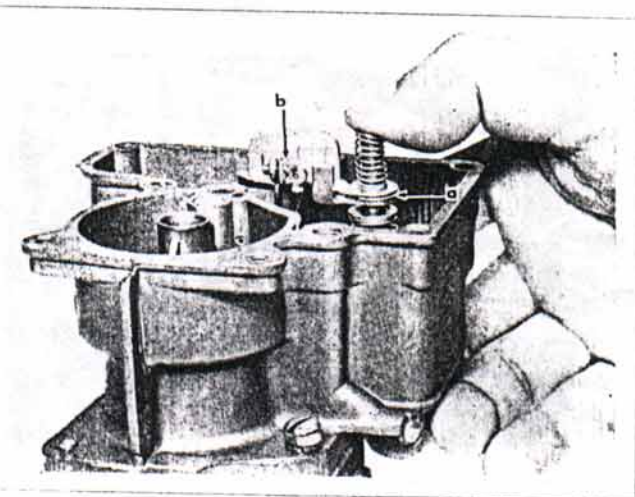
Ajuste de la varilla dosificadora del Carburador Carter YF 938-SA o 2756-S.
